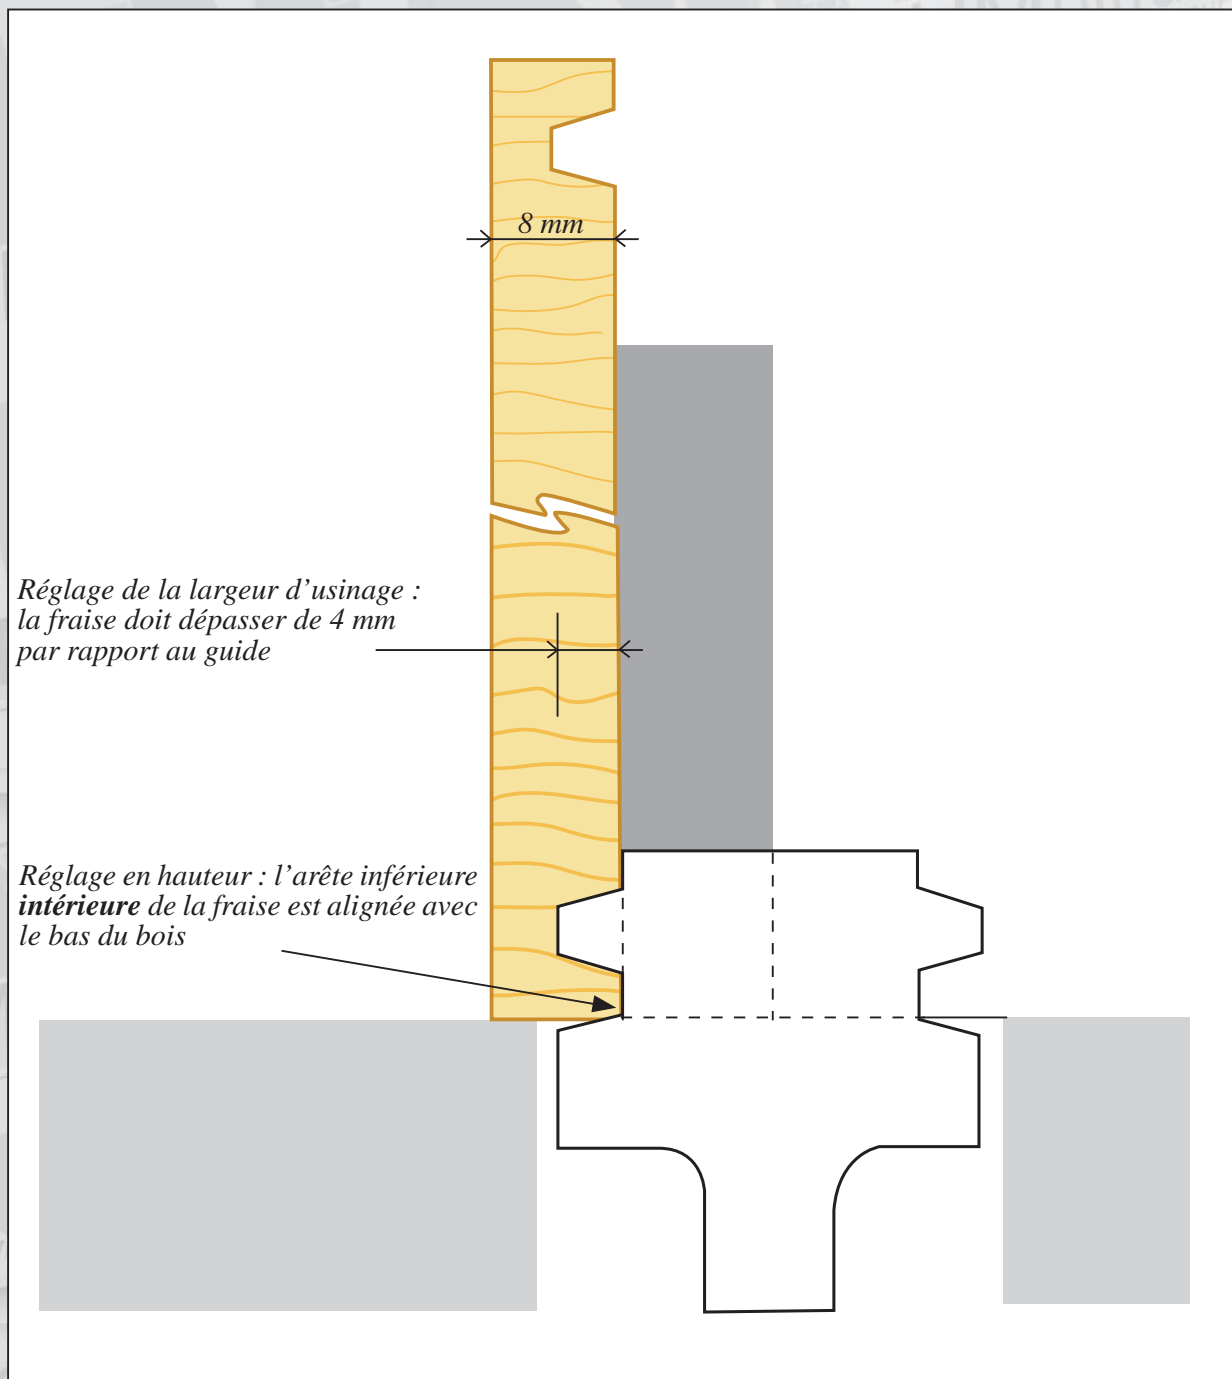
réglage de la fraise pour l'usinage des côtés (en 8 mm)
